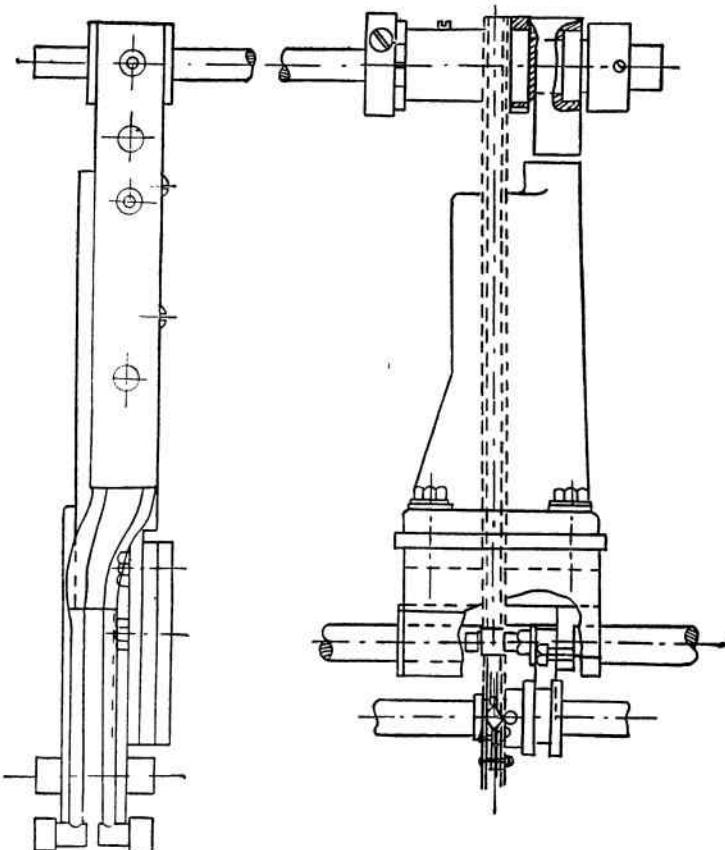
Контактная головка и устройство для подачи положительного угля дуговой лампы «Super Cinex»
